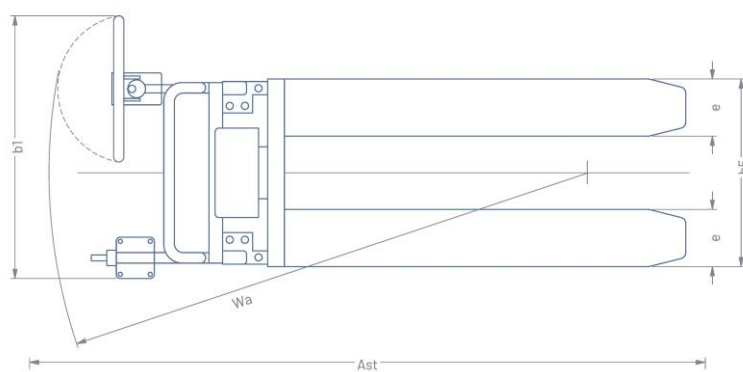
ZAC-GO Draufsicht mit Kürzeln
